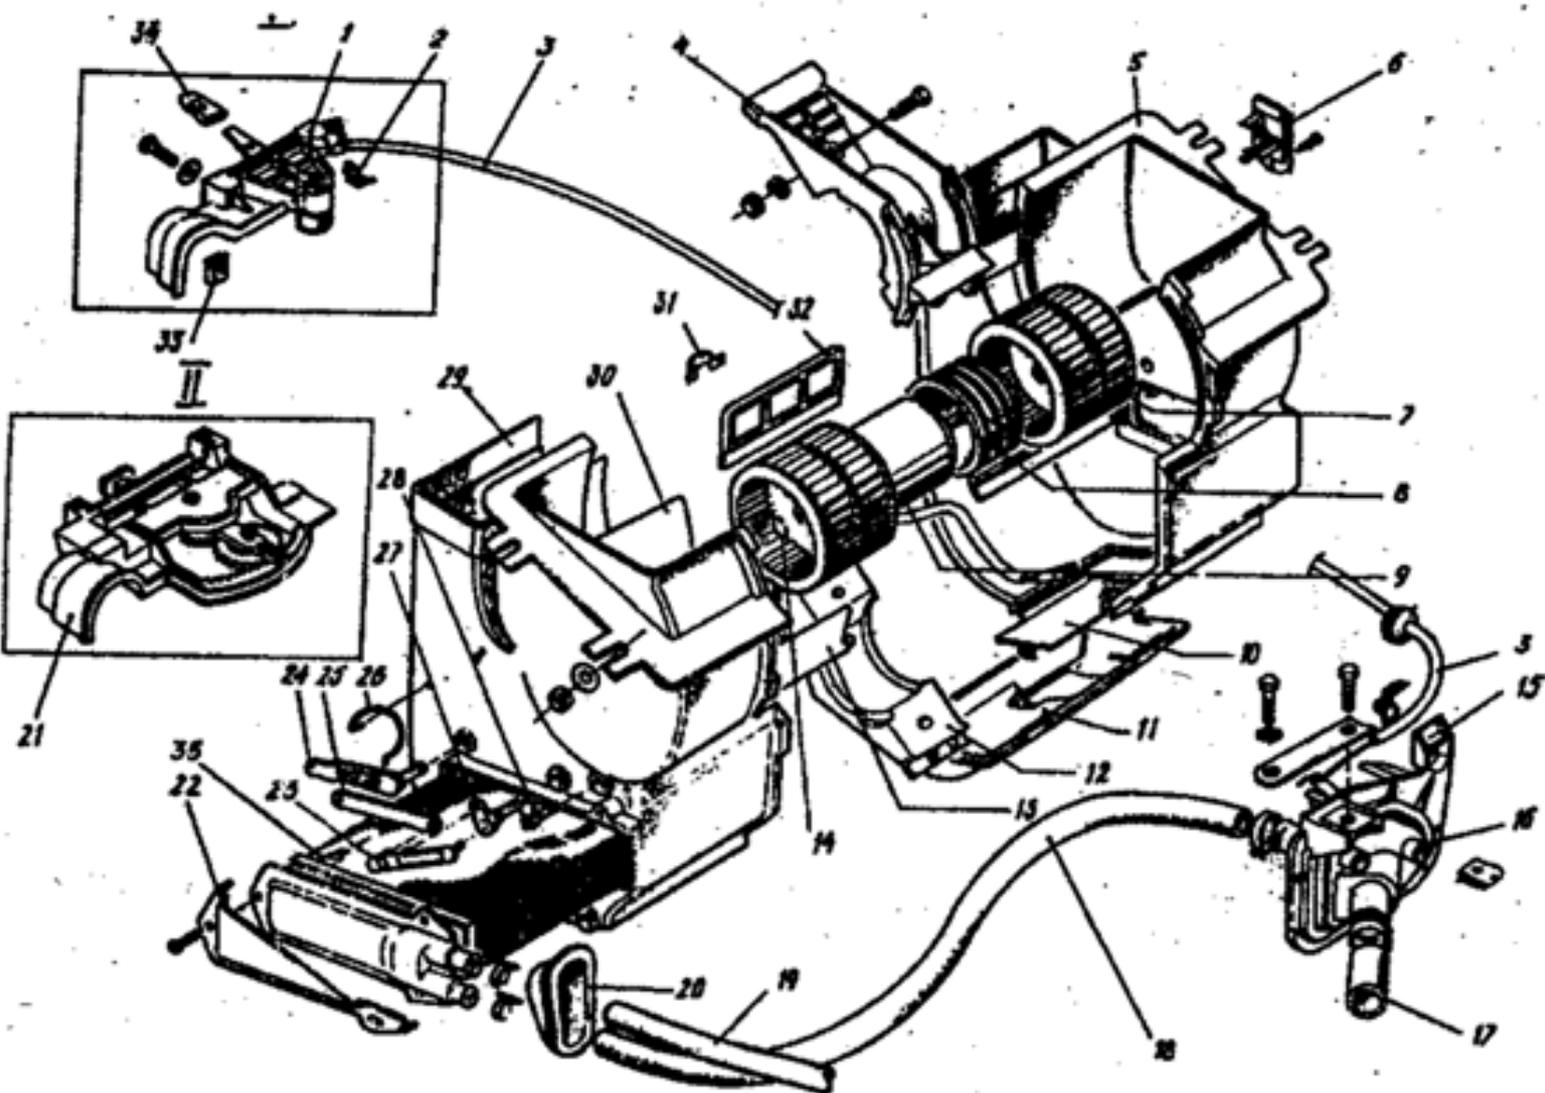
Детали отопителя и его управление: 1 - блок управления отопителем; 2 - скоба крепления тяги; 3 - тяга; 4 - кожух верхний; 5 - кожух левый; 6 - резистор; 7 - колесо рабочее; 8 - прокладка; 9 - электродвигатель; 10 - вставка распределителя воздуха; 11 - распределитель воздуха; 12 - кожух нижний; 13 - заслонка задняя; 14 - кольцо стопорное; 15 - кронштейн крепления тяги; 16 - кран управления; 17 - шланг от двигателя; 18 - шланг от крана управления; 19 - шланг к двигателю; 20 - уплотнитель; 21 - блок управления отопителем (на панели приборов 11021-5325016); 22 - накладка защитная; 23, 24, 25 - рычаги привода заслонок; 26 - пружина заслонки; 27, 28 - поводки рычагов; 29 - кожух правый; 30 - заслонка передняя; 31 - скоба пружинная крепления кожухов; 32 - вставка кожуха отопителя; 33 - гайка пластинчатая; 34 - рукоятка; 35 - радиатор.
